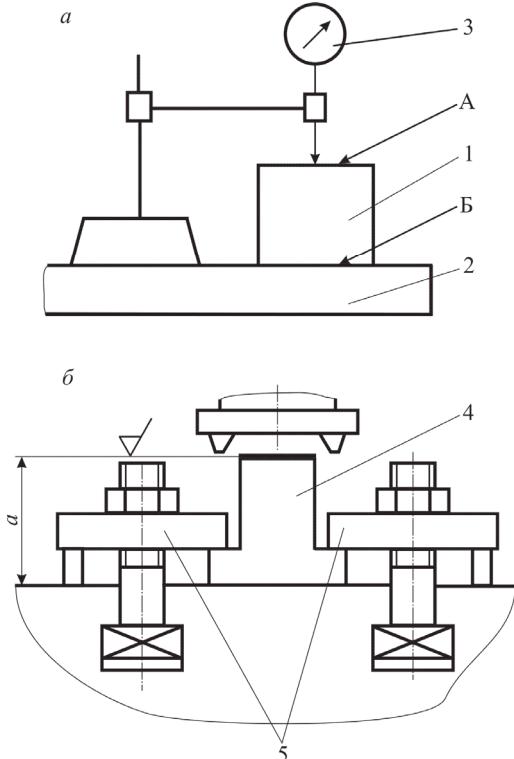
Схемы контроля заготовки 1 (а) и обработки корпуса 4 (б)
